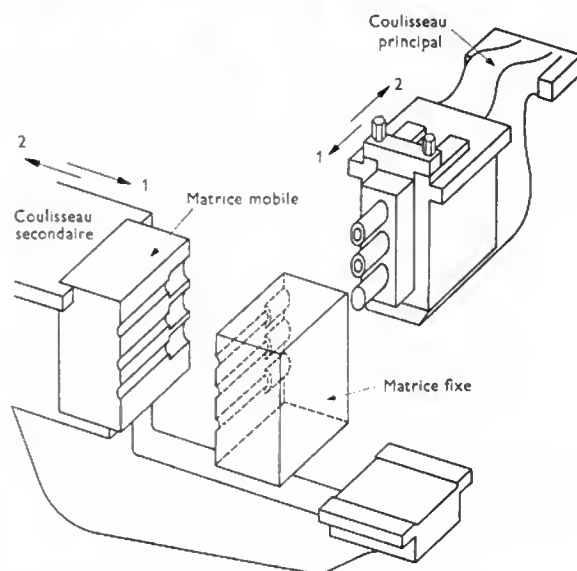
Coulisseaux d'une machine à forger horizontale
